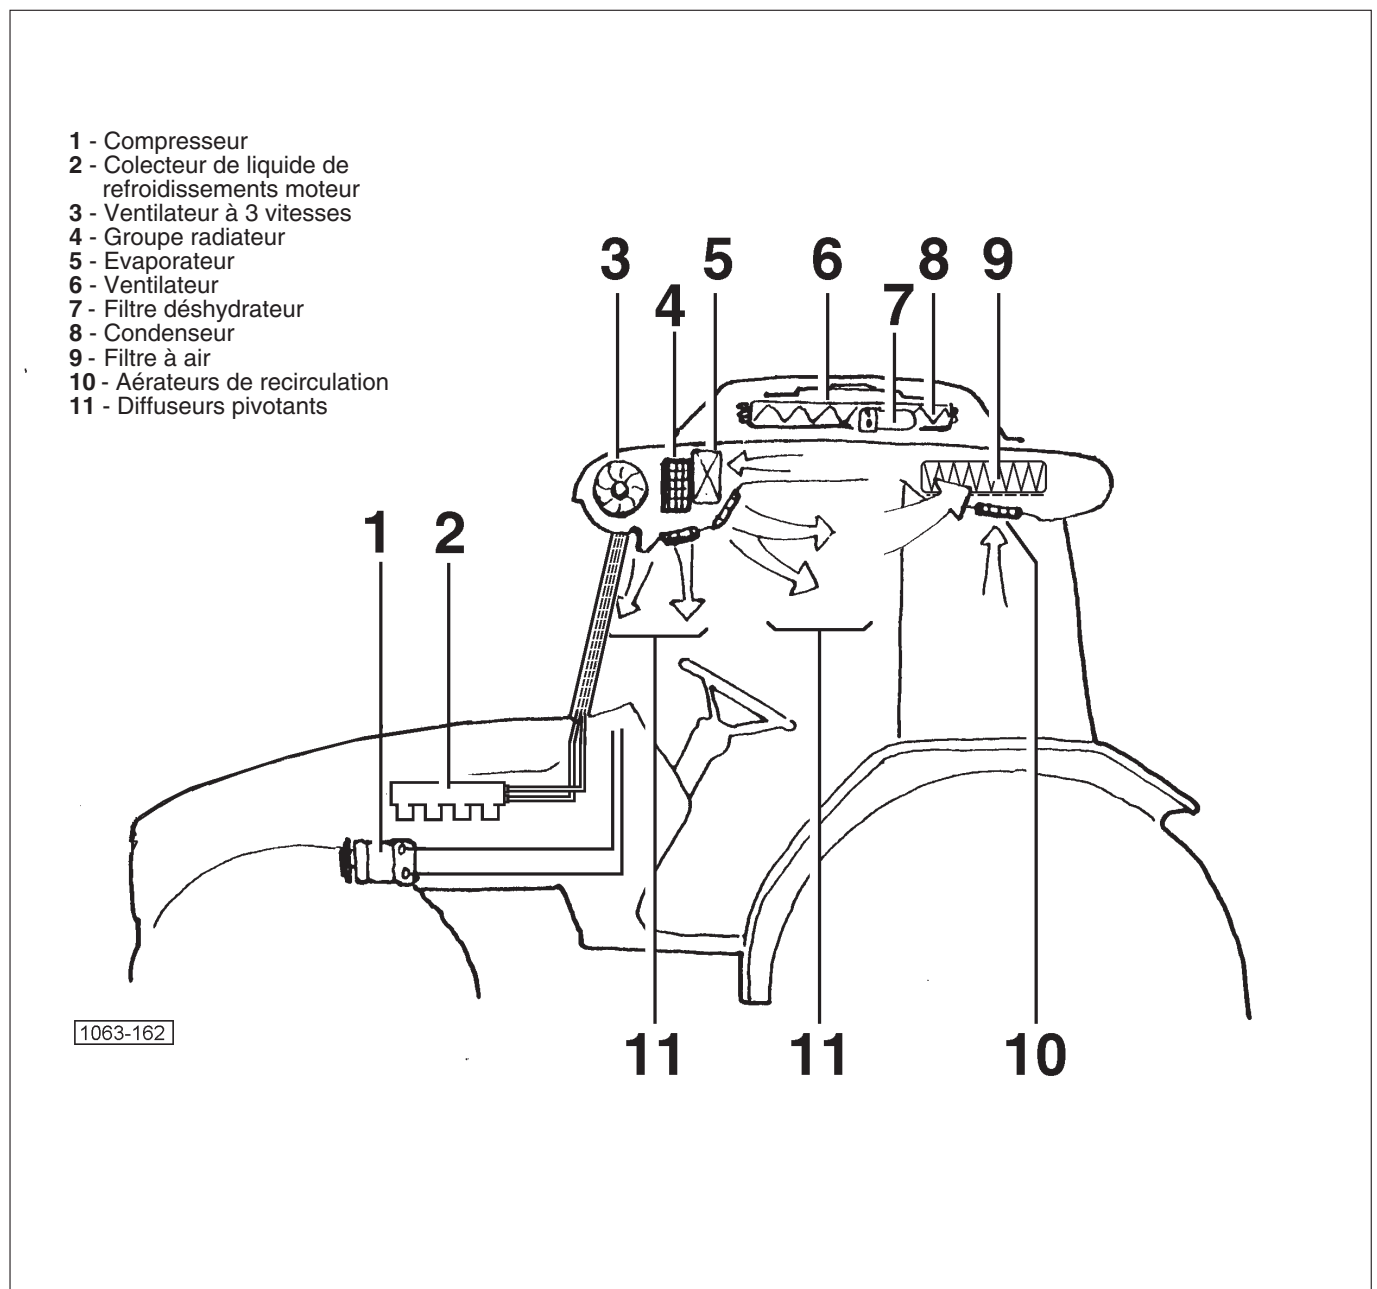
Configuration de l'installation de ventilation, chauffage.
